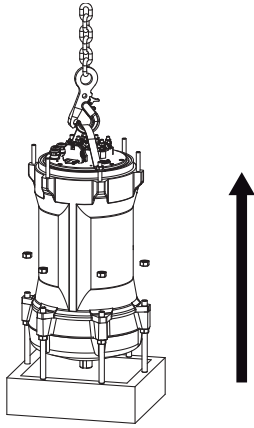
Dépose du carter de moteur (J 205, J 405)
